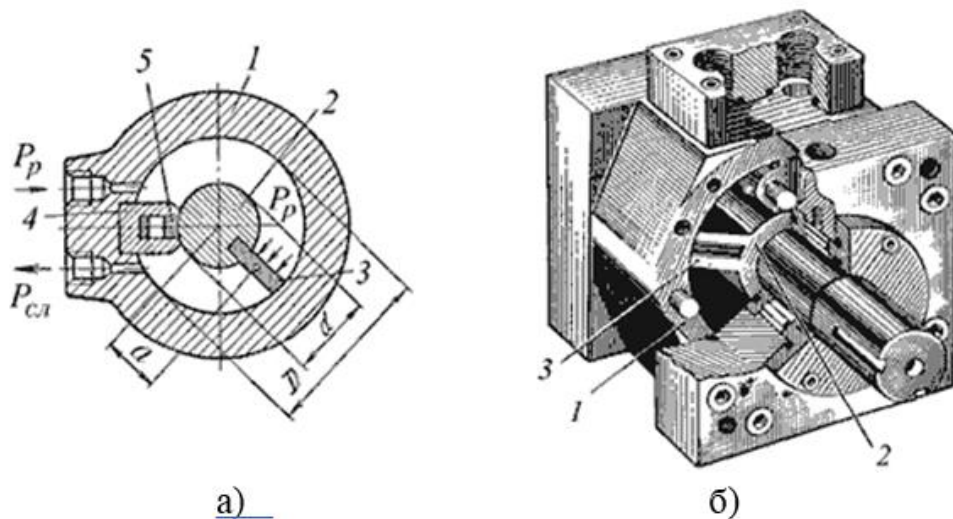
Поворотный однолопастной гидродвигатель
